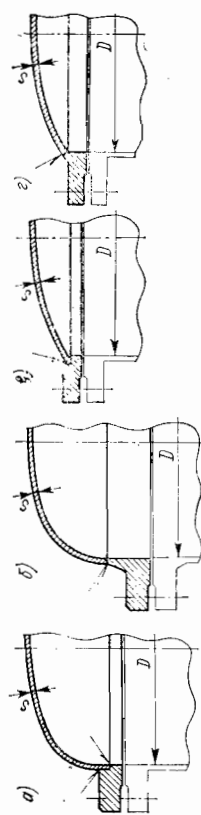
Типовые конструкции отъемных выпуклых крышек в стальных сварных аппаратах; а — эллиптическая с плоским фланцем; б — эллиптическая с фланцем, приварным встык; в — сферическая с угловым сварным соединением с фланцем; г — сферическая со стыковым сварным соединением с фланцем
